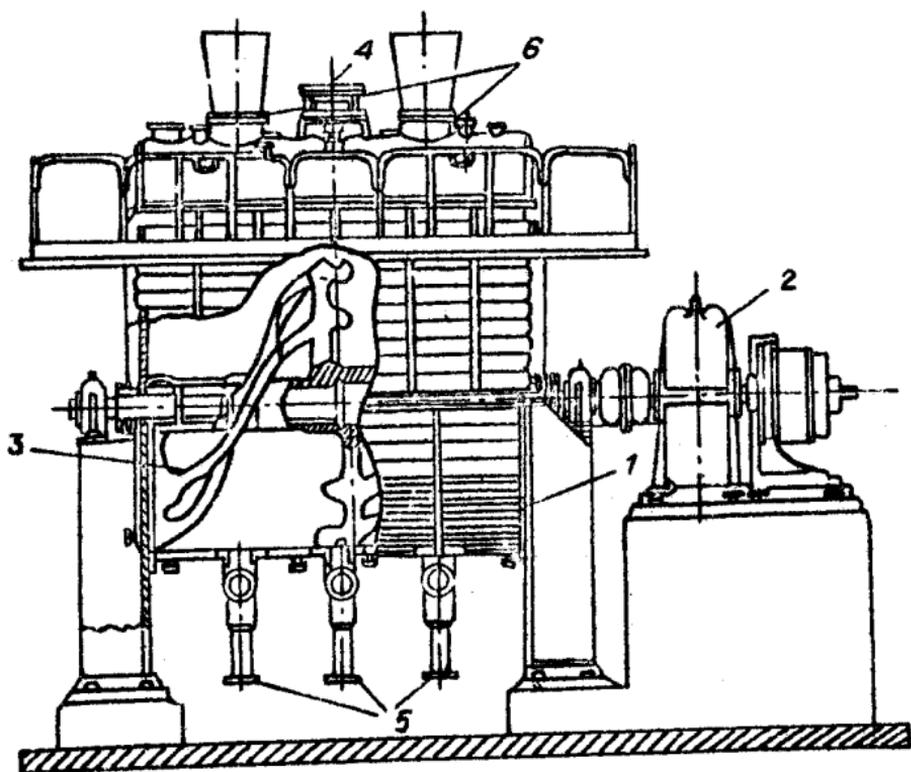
Одномешалочный ксантогенатор: 1 - корпус аппарата; 2 - привод мешалки; 3 - мешалка; 4 - загрузочный лок; 5 - штуцеры для выгрузки пульпы; 6 - противовзрывные мембраны.
